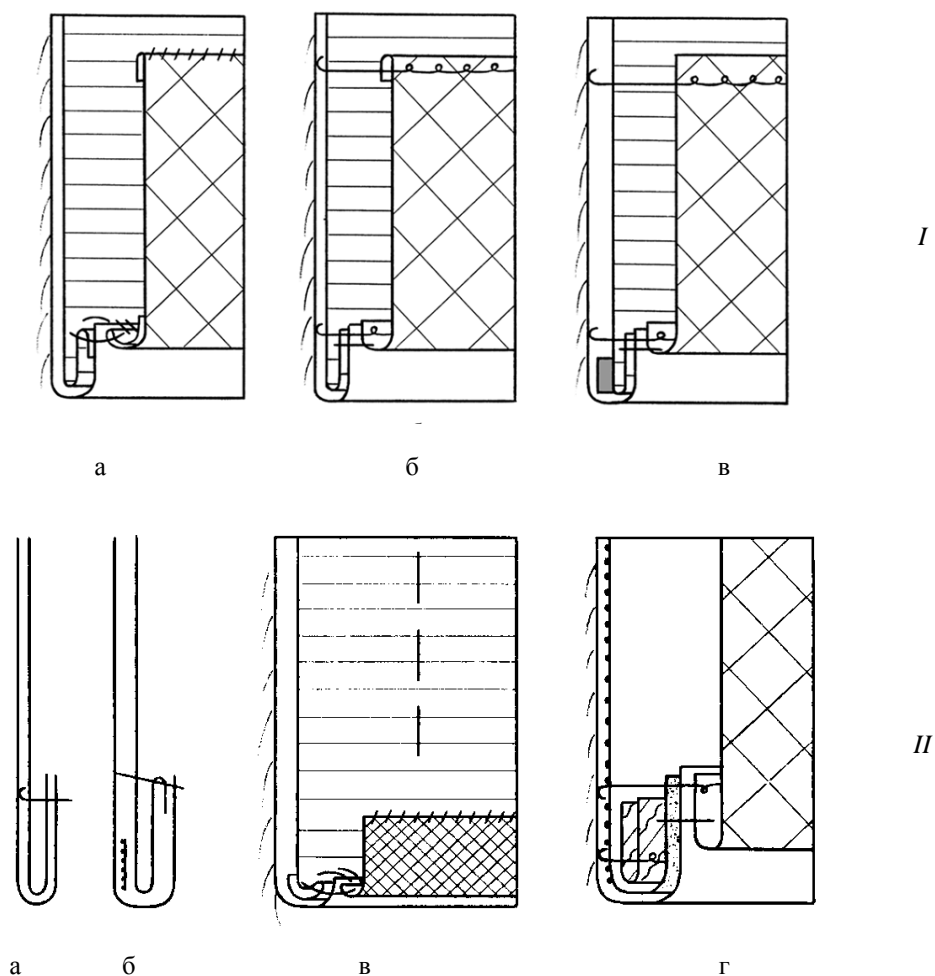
Монтажная схема конструкции низа изделия: I – с отлетной по низу подкладкой; II – с притачной по низу подкладкой
